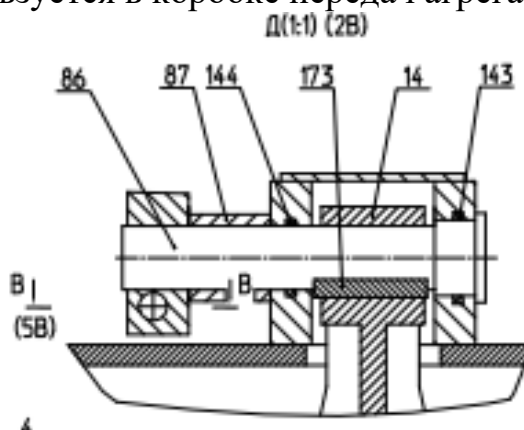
показ детали «Вилка» в сборочном чертеже (позиция 14)
